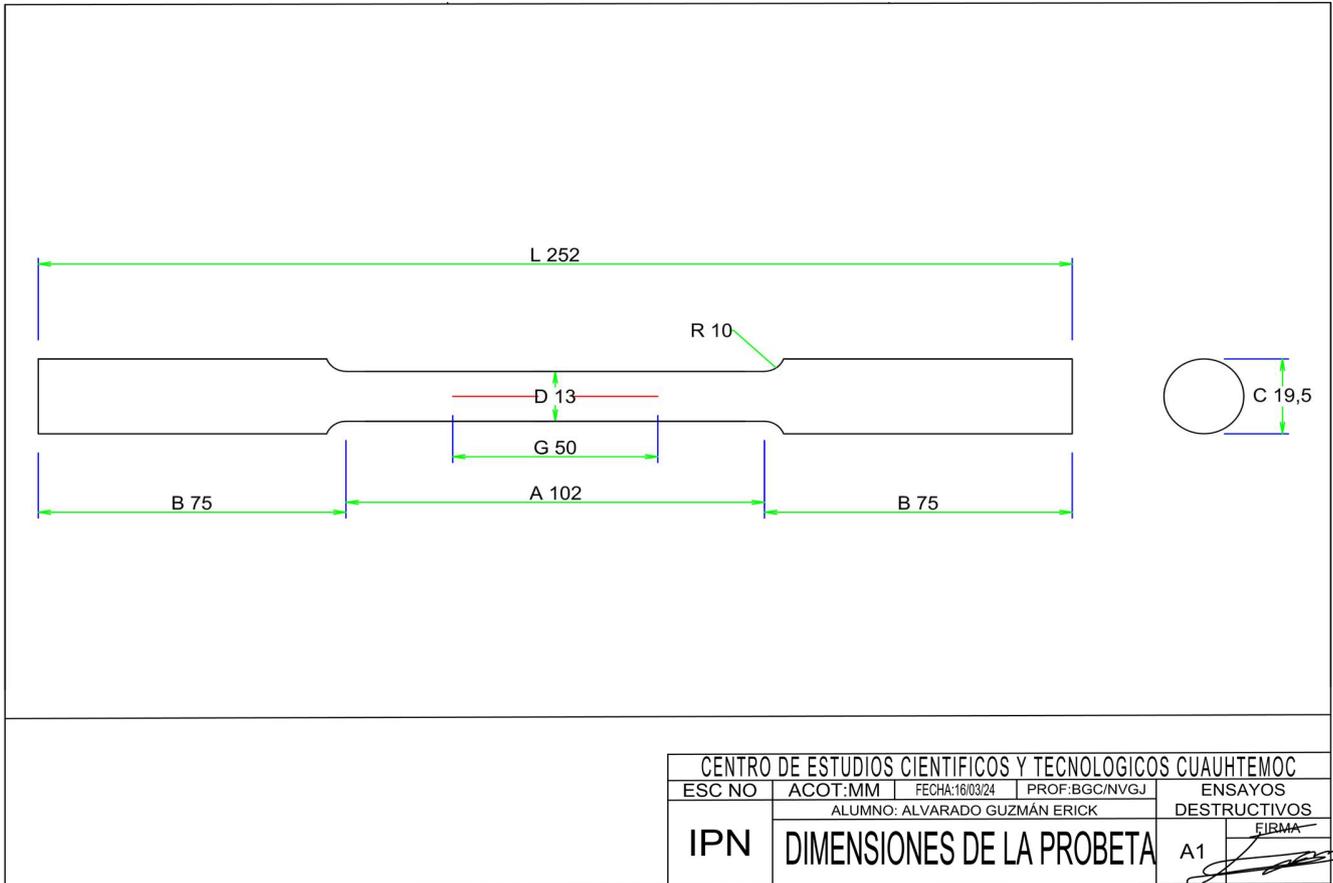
Dimensiones en la probeta de aluminio (en milímetros)
